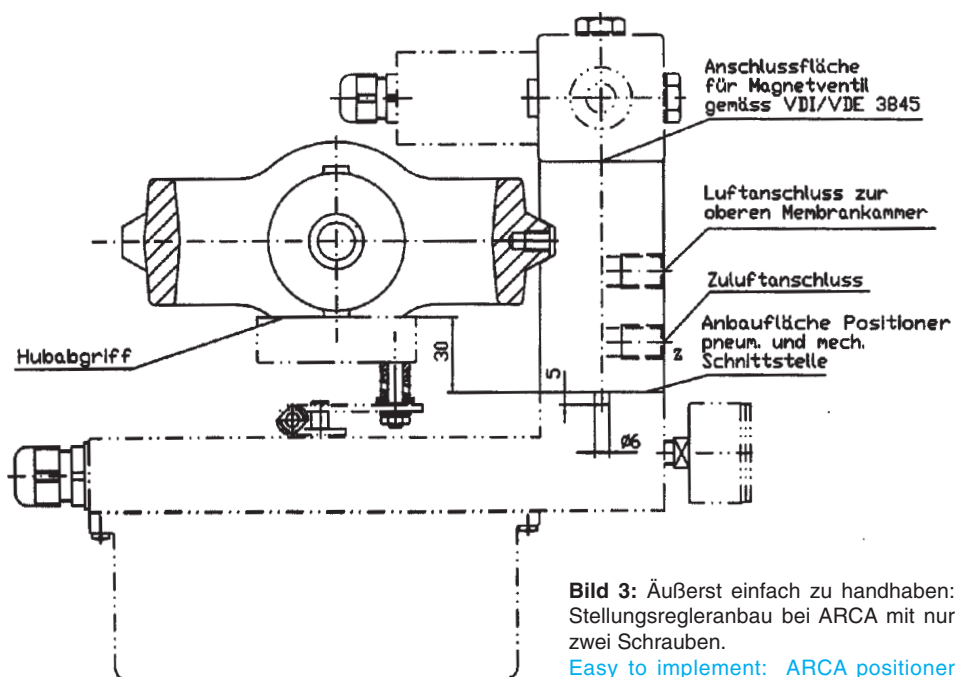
Äußerst einfach zu handhaben: Stellungsregleranbau bei ARCA mit nur zwei Schrauben.
